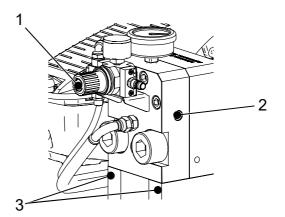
Sfiato dell'unità di stampaggio SOLIDStamp
